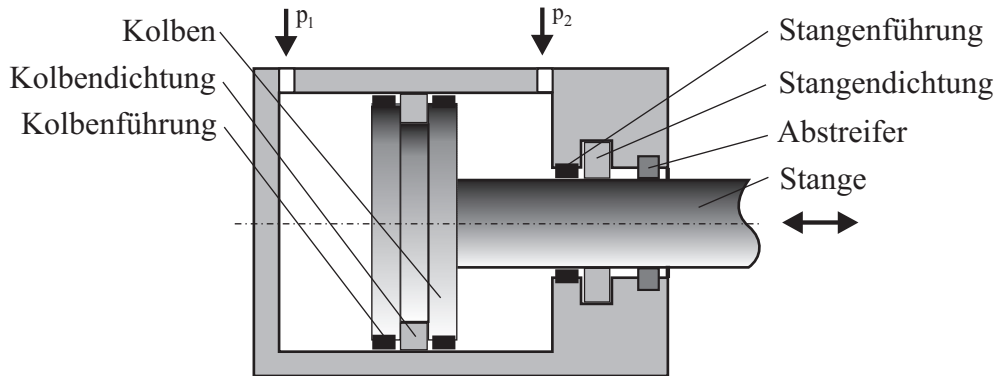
Hydraulikdichtungen und Führungen nach MÜLLER [57]
